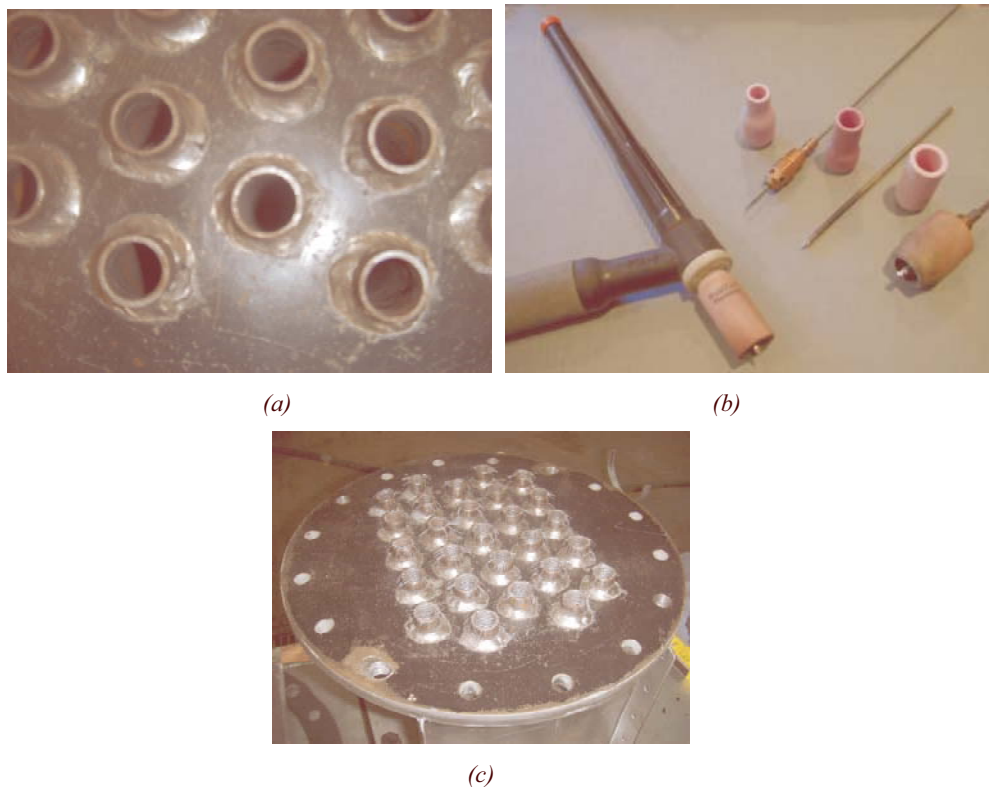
a) Soldaduras finales de los tubos aletados, b) boquilla para soldaduras de tipo Tig) y c) arreglo de tubos aletados con arañas para una caída uniforme de la película descendiente
